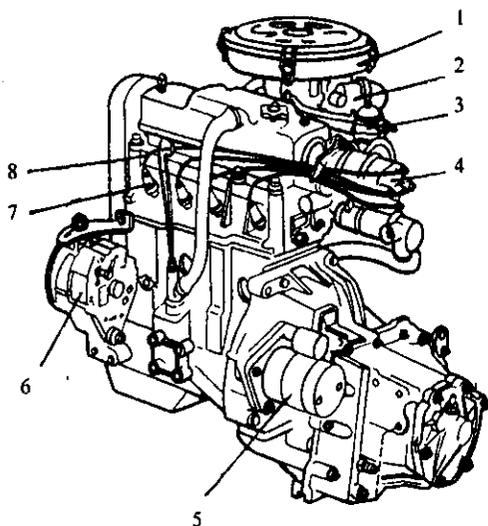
Общий вид двигателя (ВАЗ-2109):
